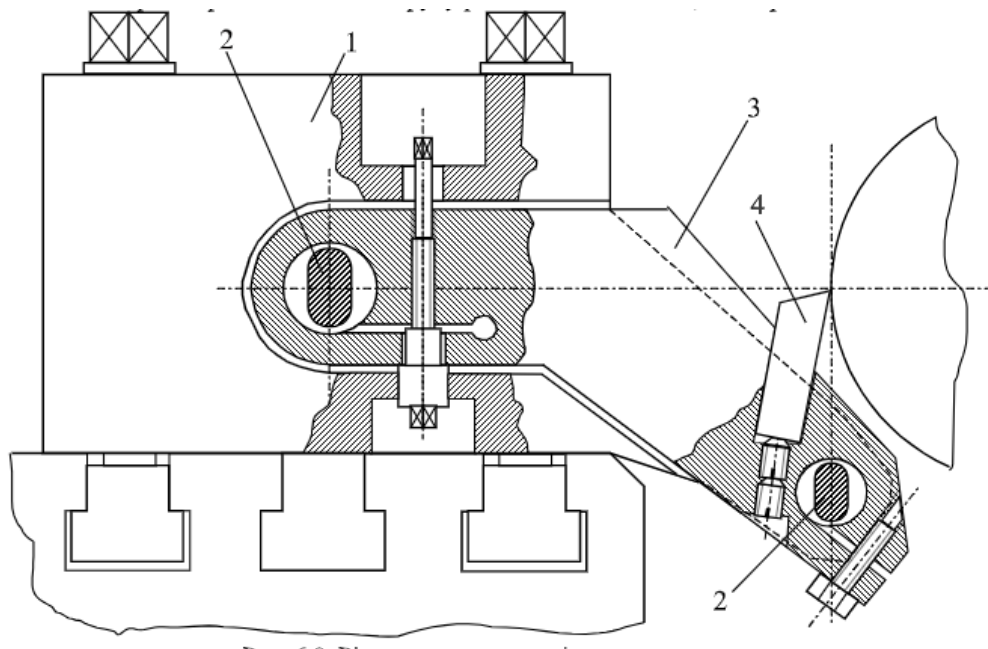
Різцетримач з пристроєм для дроблення стружки
